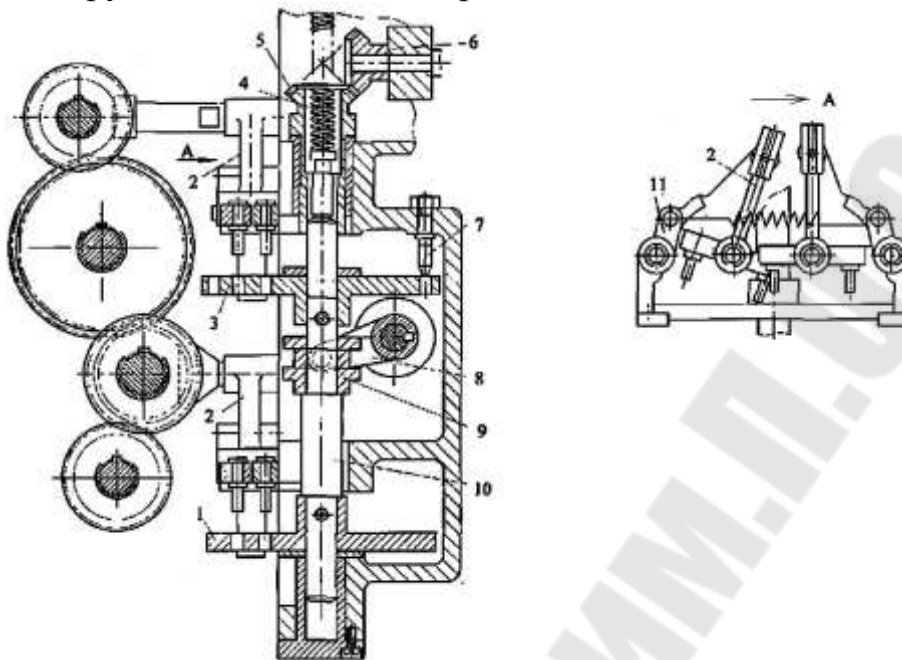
Механизм преселективного управления коробкой скоростей токарно-винторезного станка
